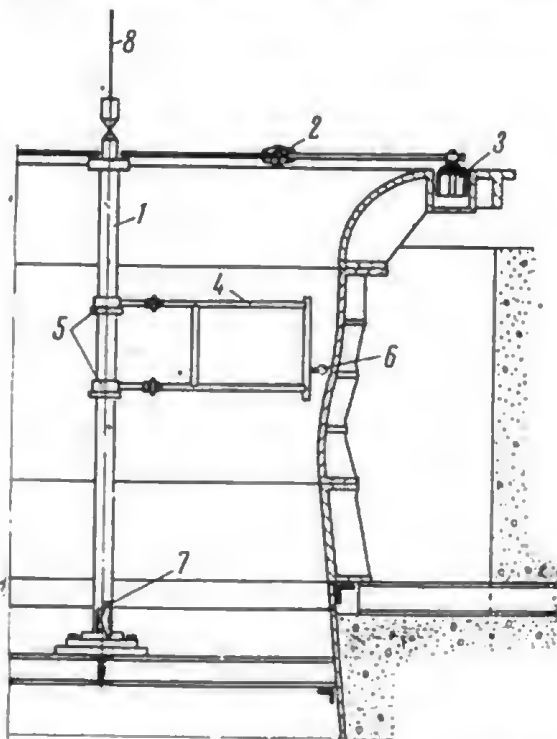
Проверка цилиндричности камеры рабочего колеса.
